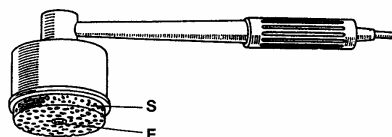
Soldadora de puntos para el regresamiento de la lámina.
